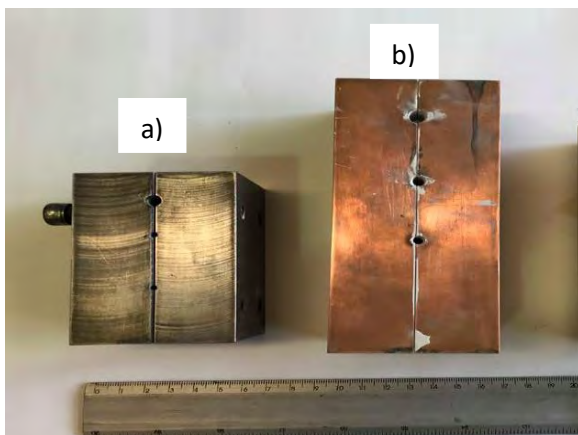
Moldes utilizados durante la solidificación del latón, a) Molde de acero y b) Molde de cobre.
